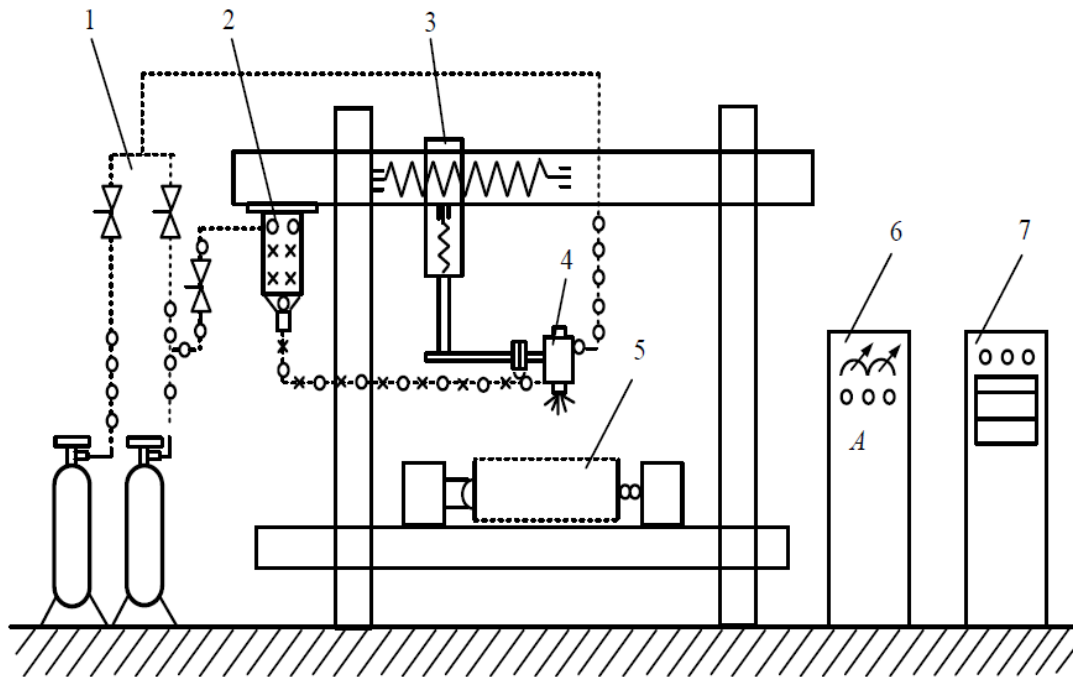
Принципова схема установки плазмового напилення УПУ-3Д
